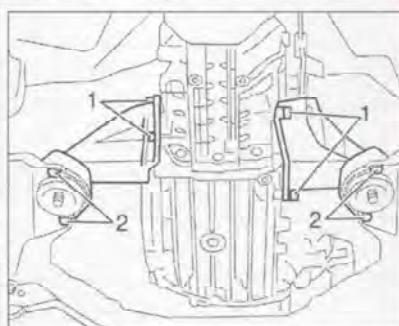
Отверните болты крепления (1 и 2) и снимите опоры коробки передач.
